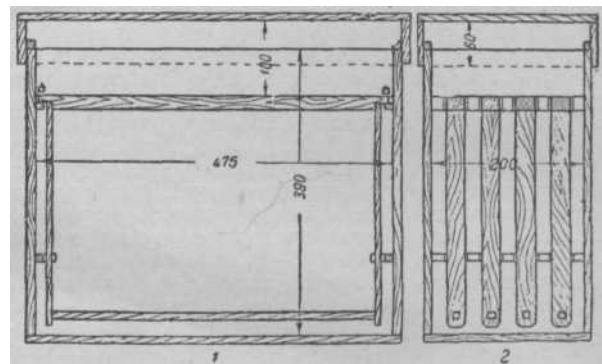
Четыреххрамочный ящик для перевозки пчел: 1 — продольный; 2 — поперечный разрез.
